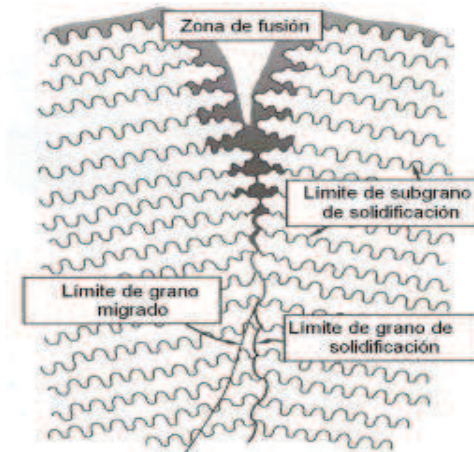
Esquema de los límites en el metal de soldadura que solidifica principalmente austenita (modo A y AF)<sup>37</sup>.
